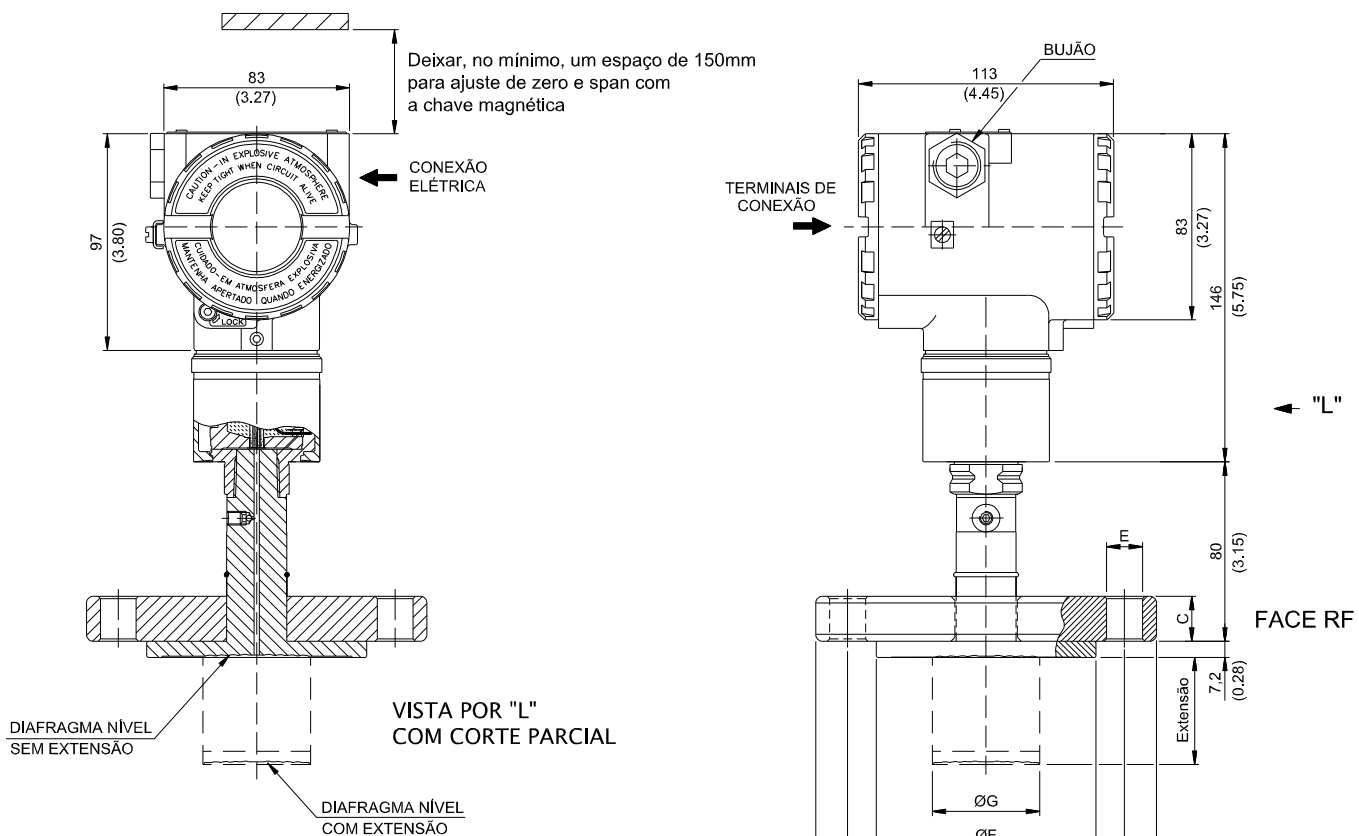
(b)– Desenho Dimensional e Posição de Montagem para o LD293 – Transmissor Sanitário
